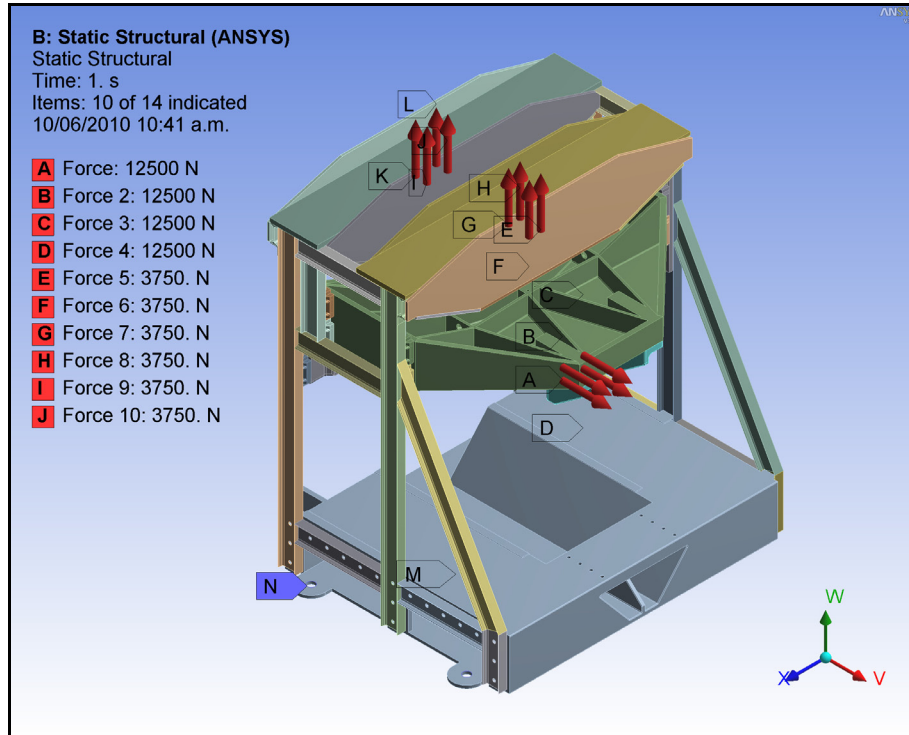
Estructura soporte – Cargas y Restricciones CI.
